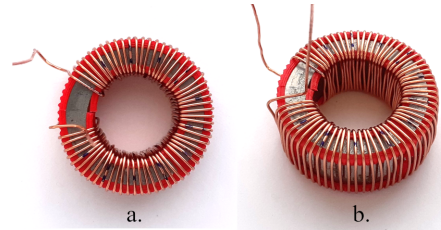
Tore équipé des écarteurs de spire et bobiné : a. vue de dessus, b. vue de devant
